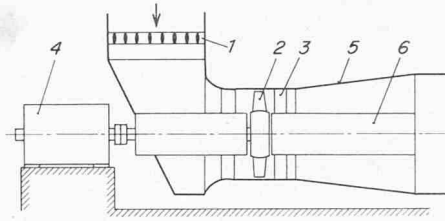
Axialventilator mit saugseitigem Umlenkkasten; der Antriebsmotor liegt ausserhalb des Ventilators
